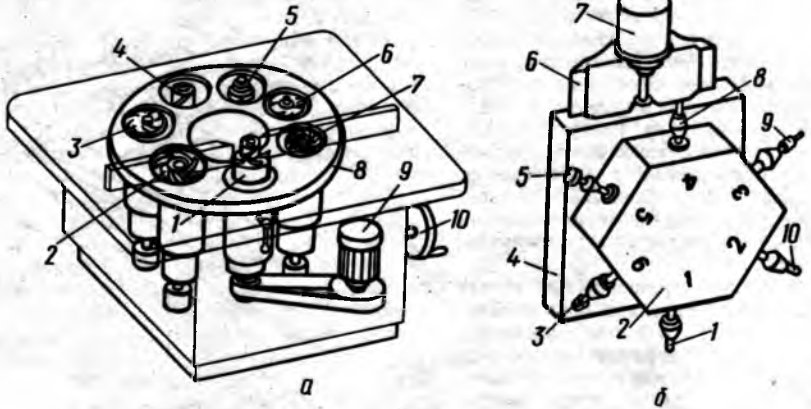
Схемы магазинов быстрой смены деревообрабатывающего инструмента: а — барабанного; б — револьверного
